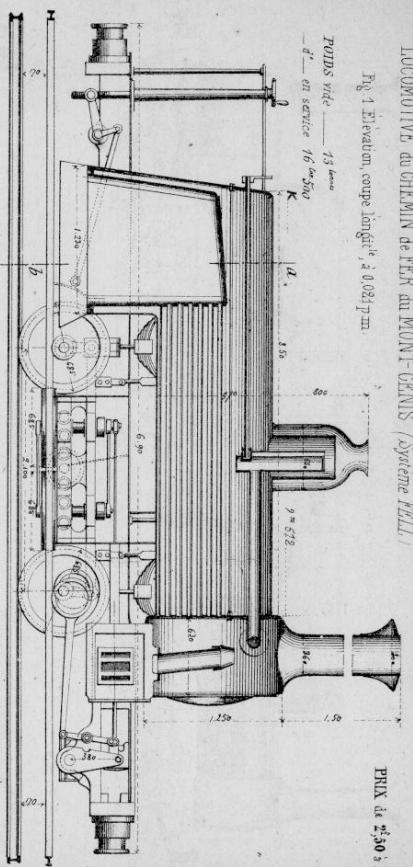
Elevation, coupe longitudinale à 0.021 p.m.
